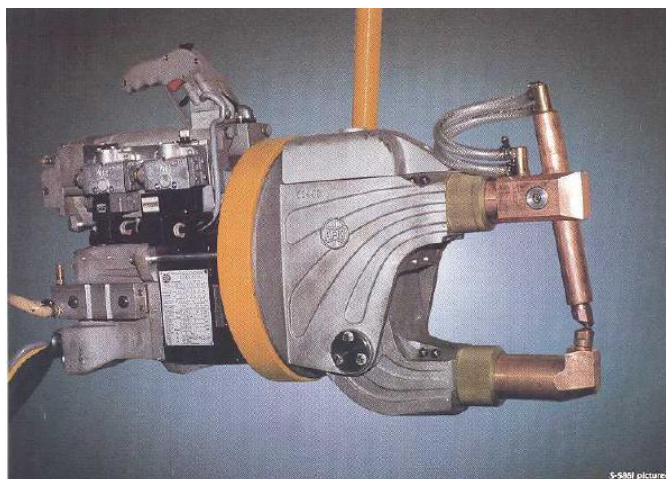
Клещи сварочные S 5861
